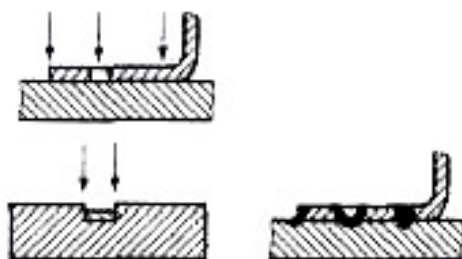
Типы сварных соединений тонких плоских деталей с массивными
